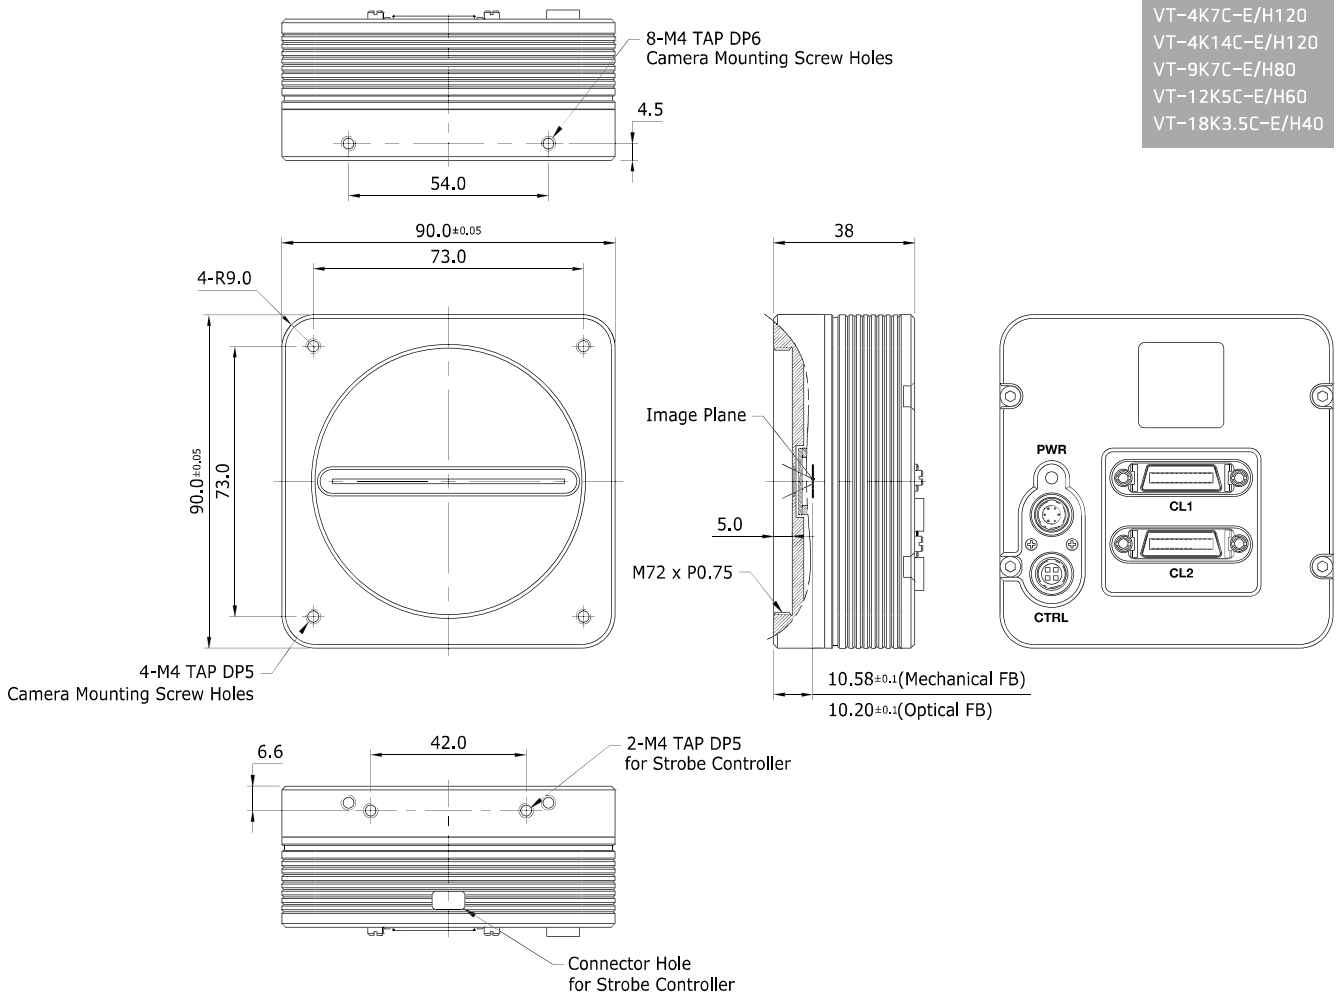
M72 mount 지원 VT CL Series Mechanical Dimension
